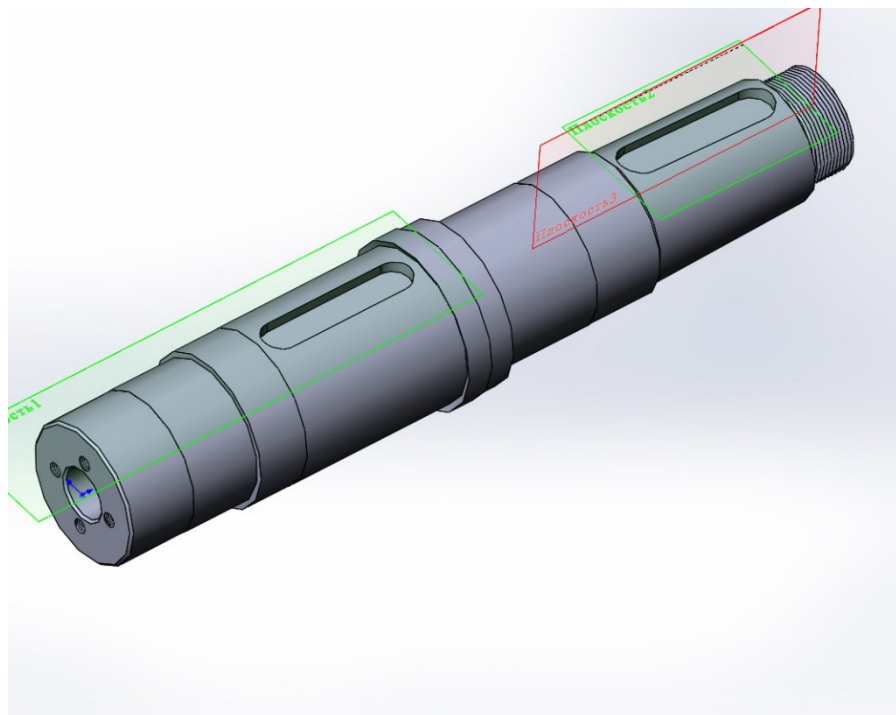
3D модель деталі «Вал РЦО-1,53»
